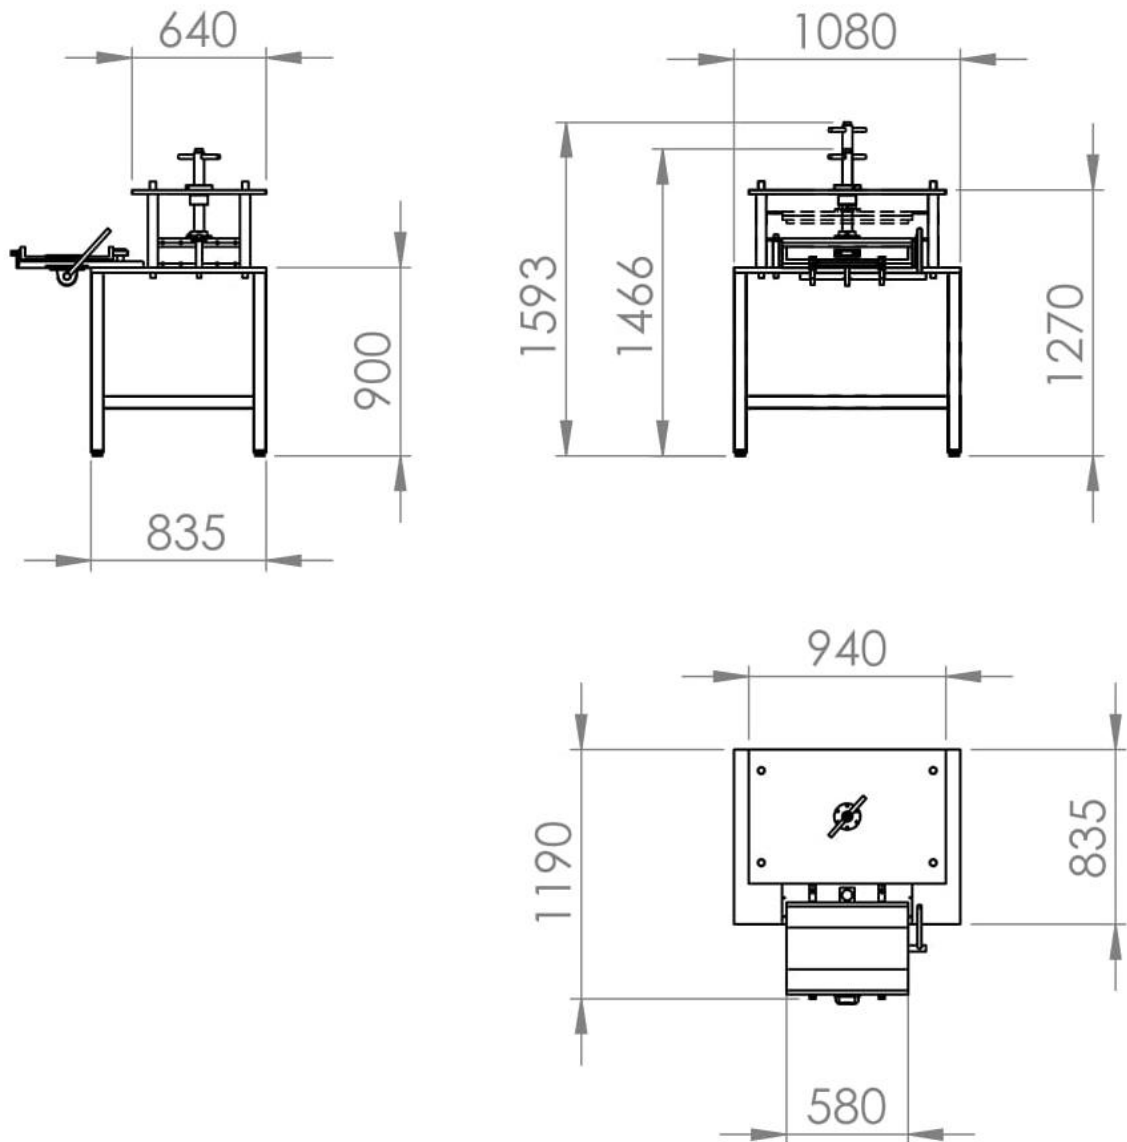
"Vistas frontal, lateral e de topo do conjunto "
